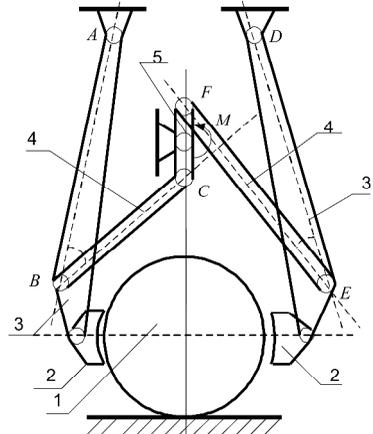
Схема механического рычажного привода к тормозным колодкам колеса экипажа:
